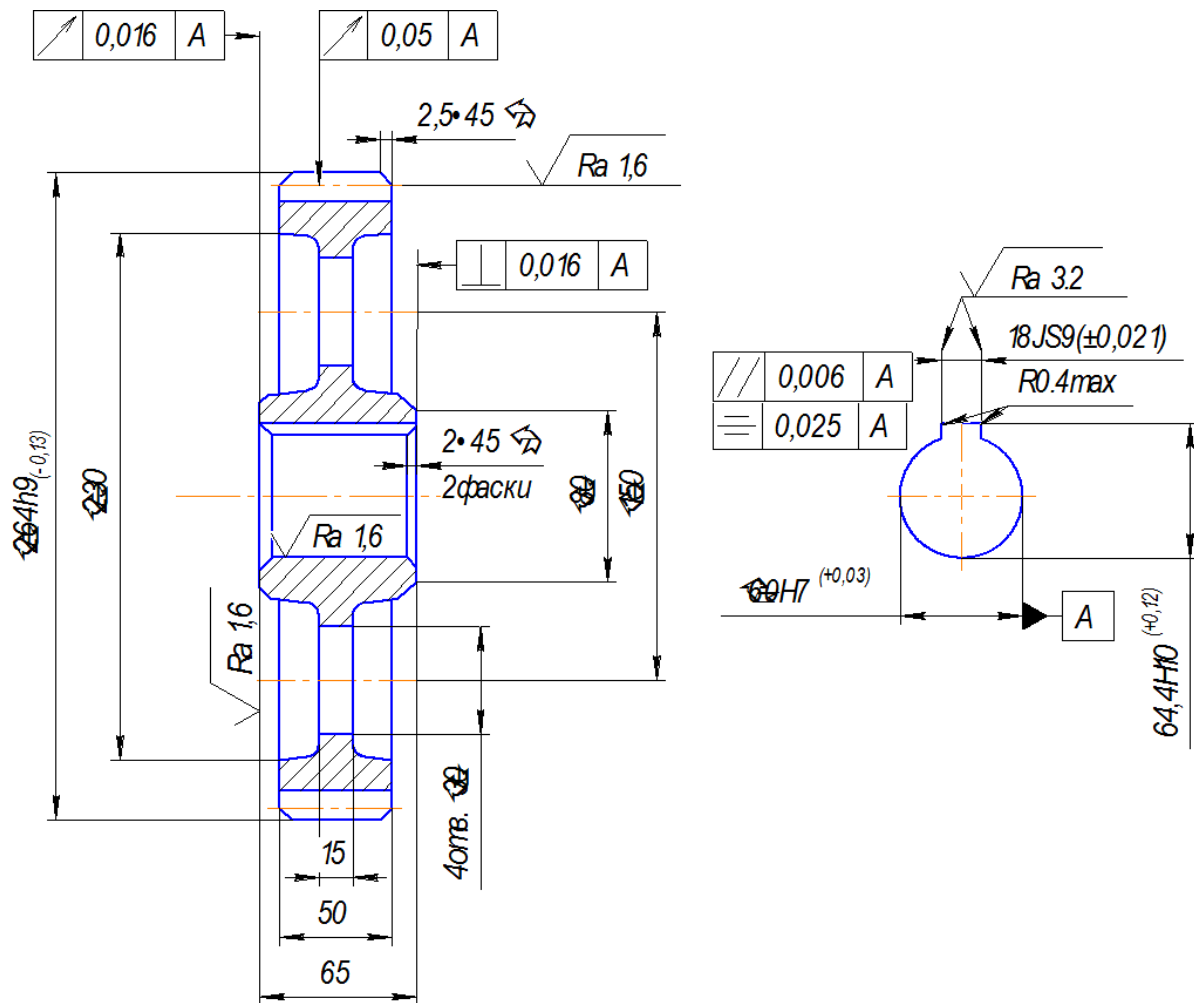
Зубчатое колесо с типовыми требованиями к точности
